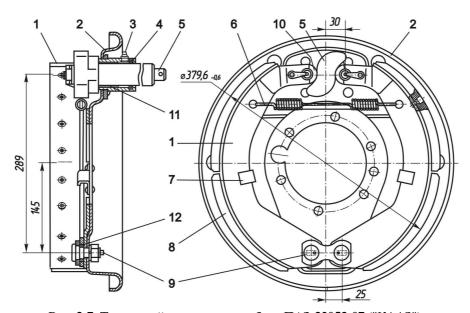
Тормозной механизм автобуса ПАЗ-32053-07 ("КААЗ")
